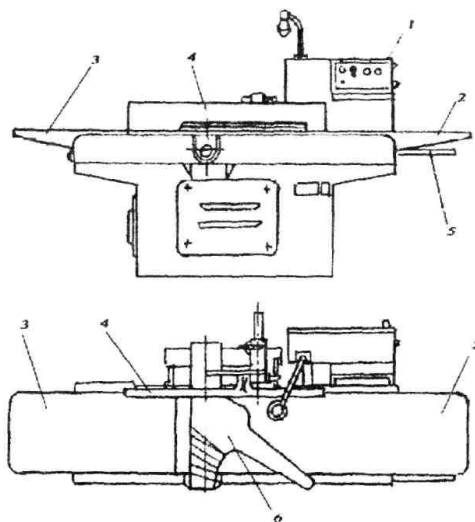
Загальний вигляд верстата СФ4-1А
